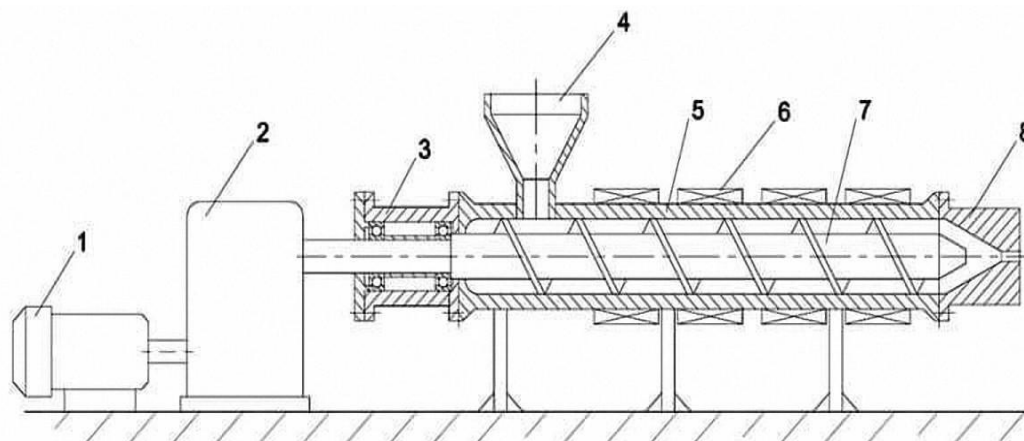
Экструдер для переработки полиэтилена и полипропилена: 1 – электродвигатель; 2 – редуктор; 3 – подшипниковый узел; 4 – загрузочный бункер; 5 – корпус; 6 – электронагреватель; 7 – шнек; 8 – экструзионная головка
